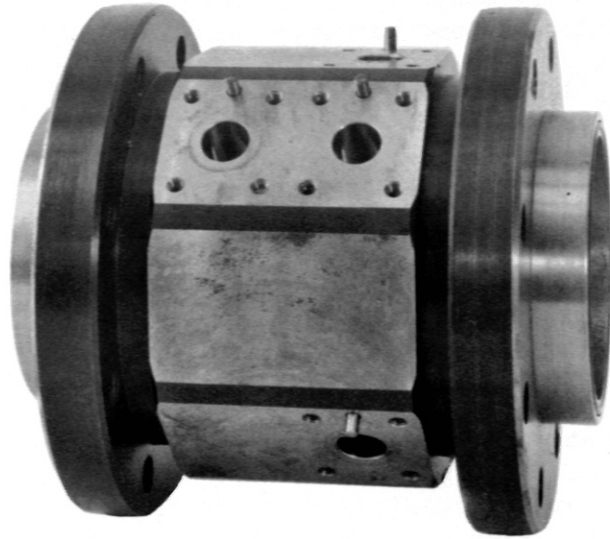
"Zwischenstück" mit Bohrungen für Wärmeleitungs sonden
